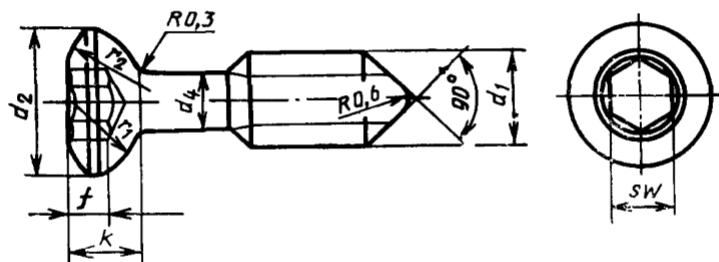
Шуруп с глубокой резьбой (НВ)
